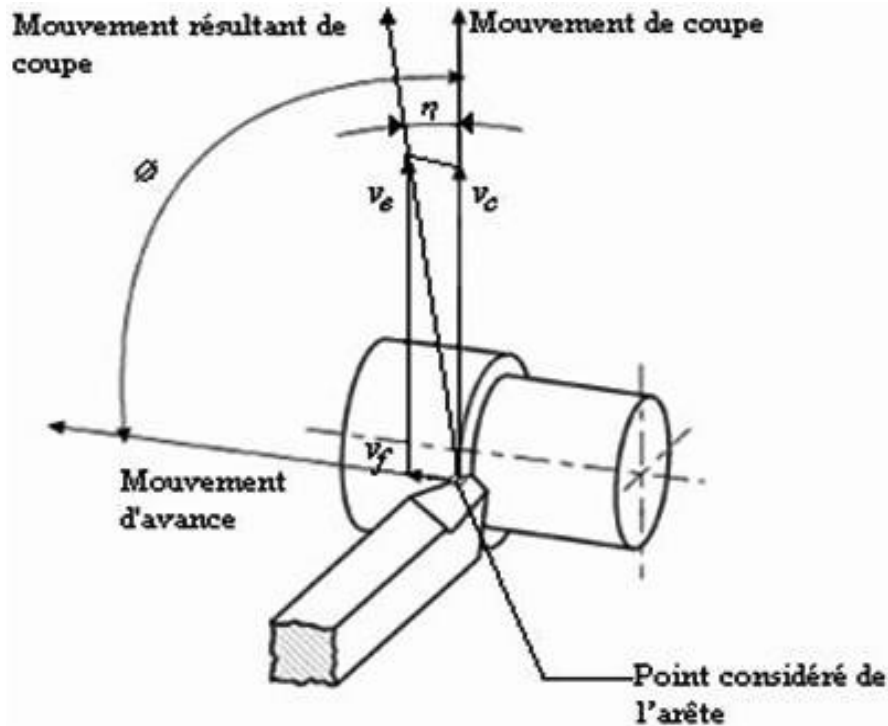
Mouvements de l'outil et de la pièce en tournage. [2]
